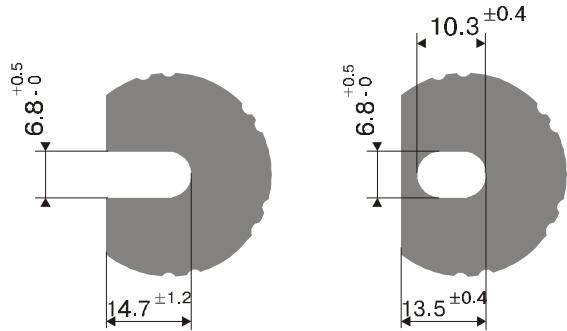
Габаритные размеры крепежных отверстий для установки оборудования в 19-дюймовом конструктиве
